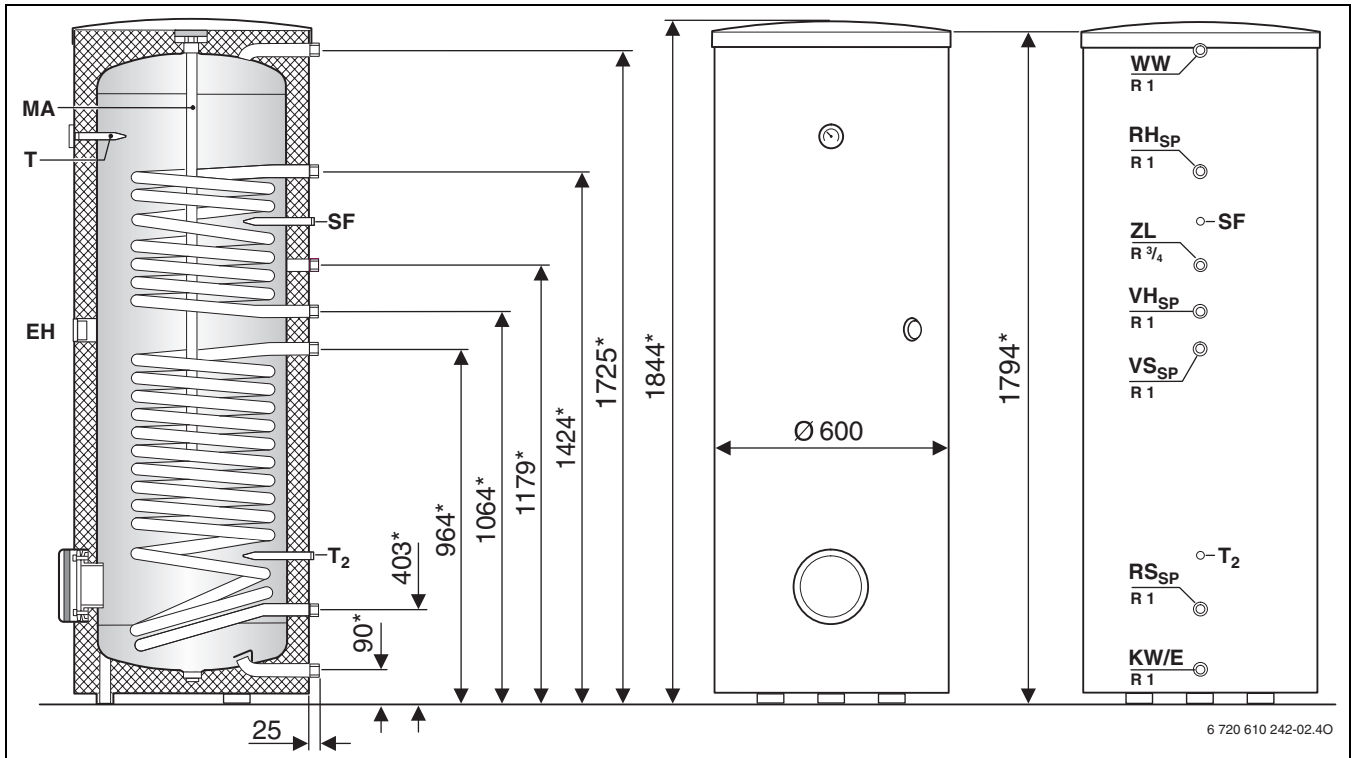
Габаритные и присоединительные размеры WST SK 300-1 solar
